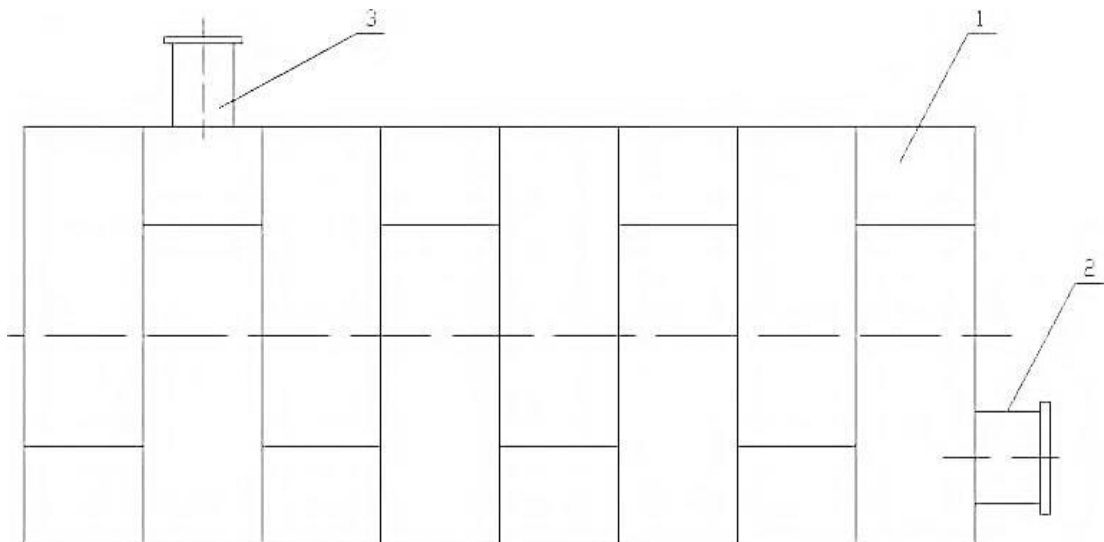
Горизонтальний циліндричний резервуар
